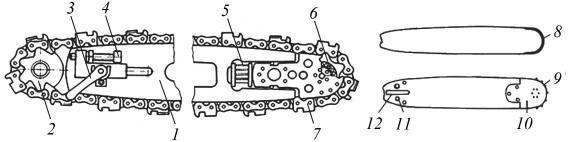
Цепной пильный аппарат моторных пил: 1 — пильная шина; 2 — ведущая звездочка; 3 — рукоятка; 4 — винт с гайкой; 5 — пружины; 6 — ведомая звездочка; 7 — пильная цепь; 8 — сплошная шина с концом, армированным твердым сплавом; 9 — направляющая шины с ведомой звездочкой; 10 — концевая головка; 11 — отверстия под винты; 12 — прорезь для натяжения цепи
